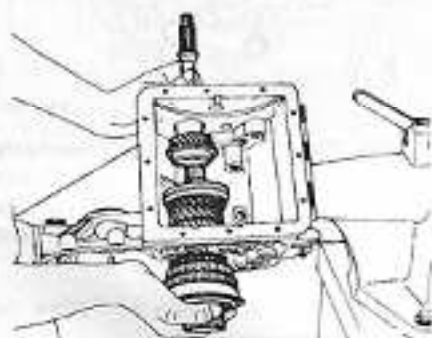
Dépose de l'arbre secondaire assemblé et de l'arbre primaire
